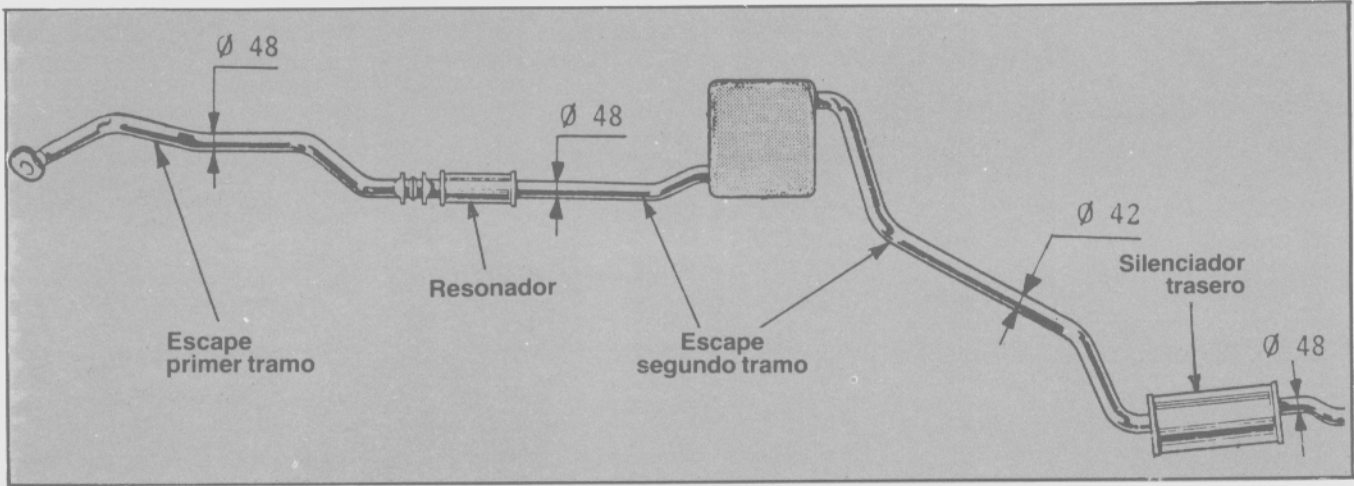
Figura esquemática del sistema de escape. Motor I4 - 2.3L
